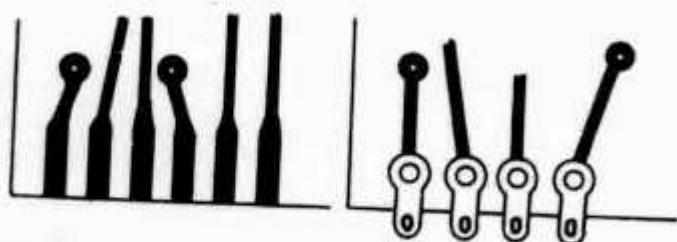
Zuführungen zu gedruckter Schaltung mit Steckkontakte und mit Lötösen.
